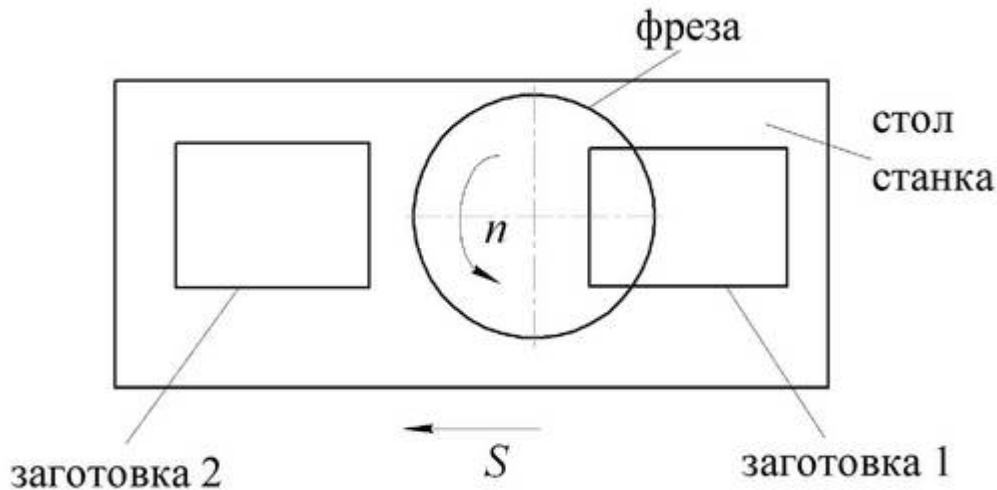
Маятниковая обработка на продольно-фрезерном станке (вид сверху)
